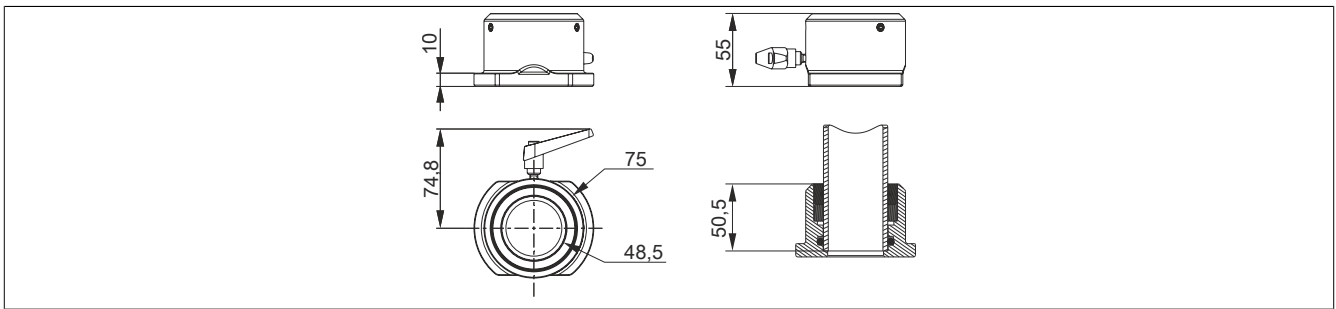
5ACCFL00.0000-000 - Abmessungen
